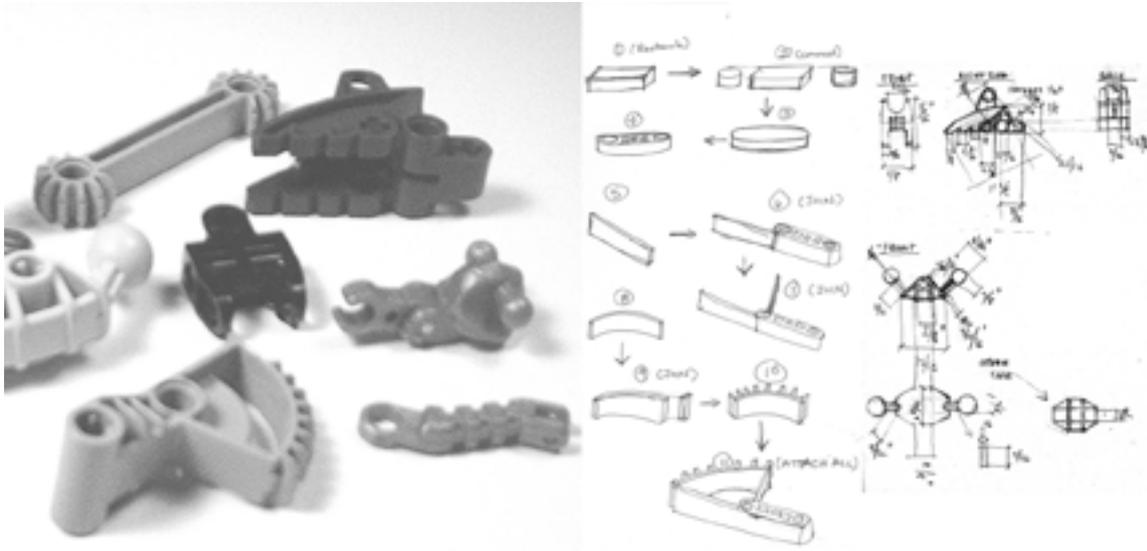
Piezas surtidas que serán la estructura del juguete arquitectónico.
